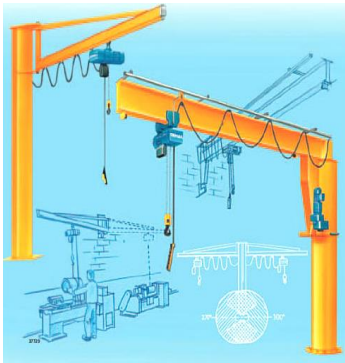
Виды консольных поворотных кранов: на неподвижной колонне и с перемещением вдоль стены цеха.
